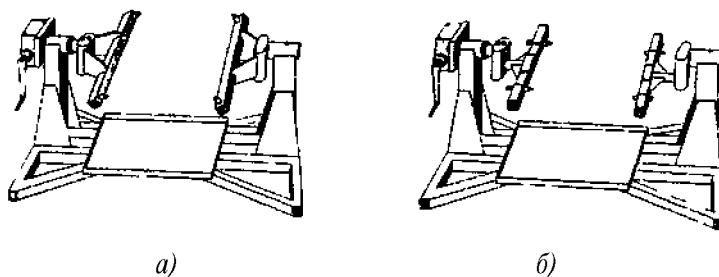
Общий вид *стендов* для разборки-сборки двигателей:
